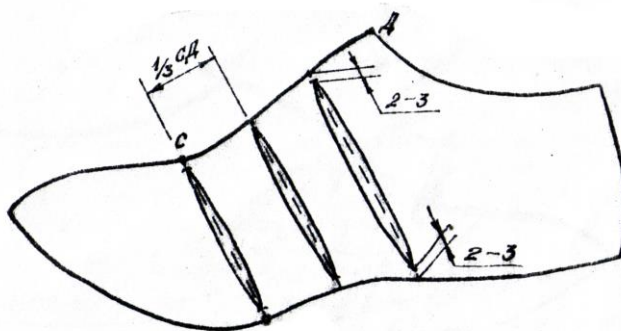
Розмітка колодки для копіювання бічної поверхні.
